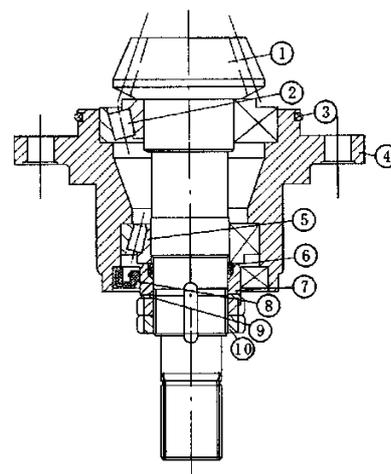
18. Крепление подшипника ведущей конической шестерни передней центральной передачи
